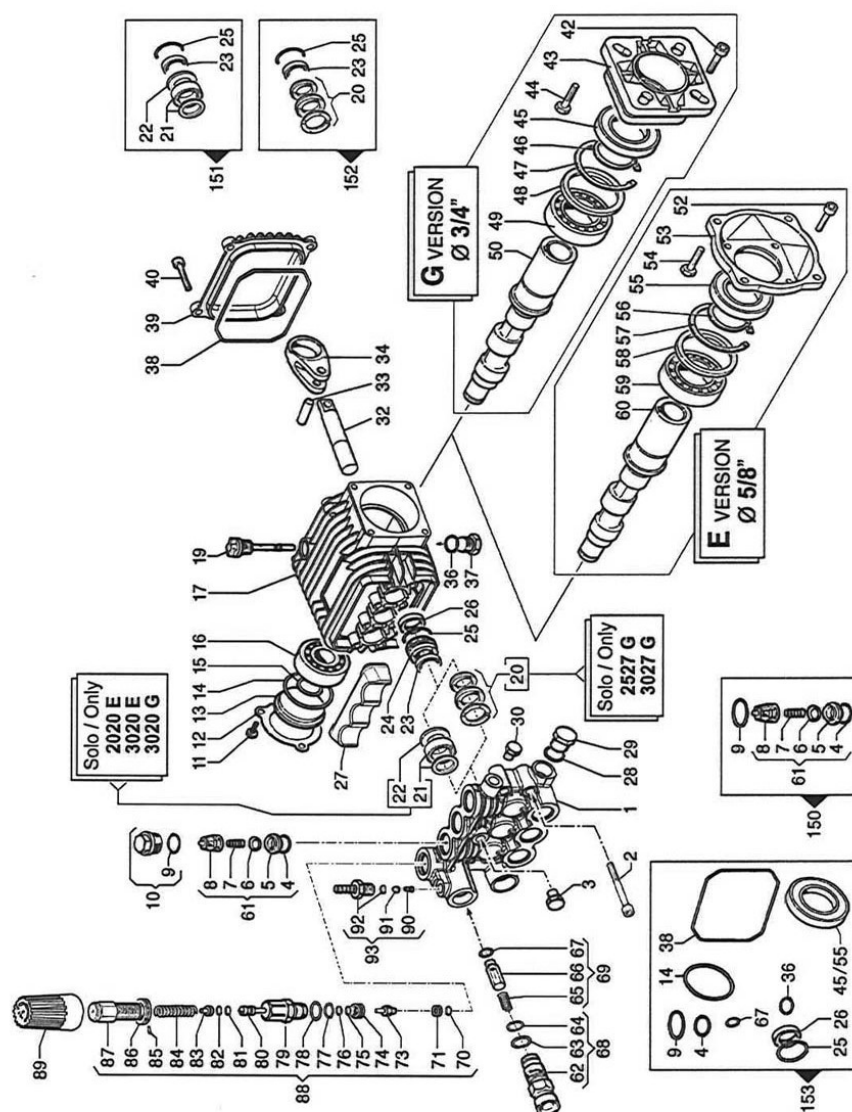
Vue éclatée de la pompe COMET BWD-K
